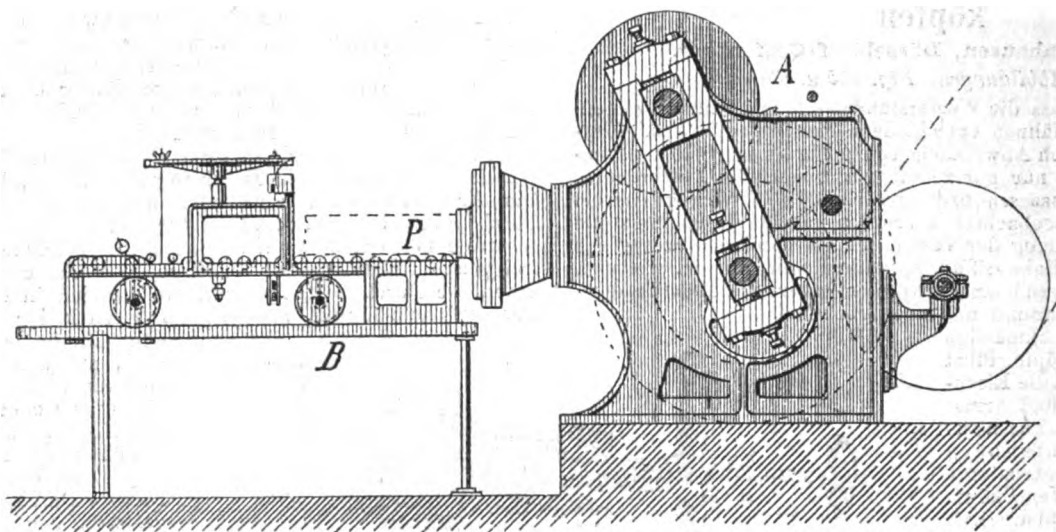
Aufsicht einer horizontalen Packet-Dachziegelpresse.
